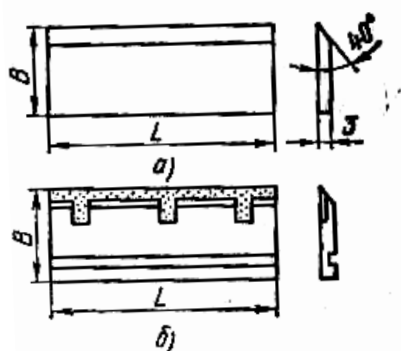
Плоские ножи с прямолинейной режущей кромкой без прорезей (а) и с пластинами из твердого сплава (б)
